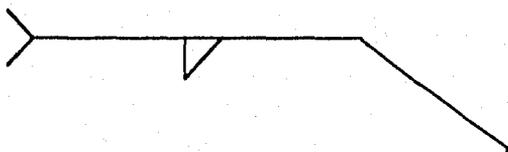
Símbolo que indica el tipo de soldadura
